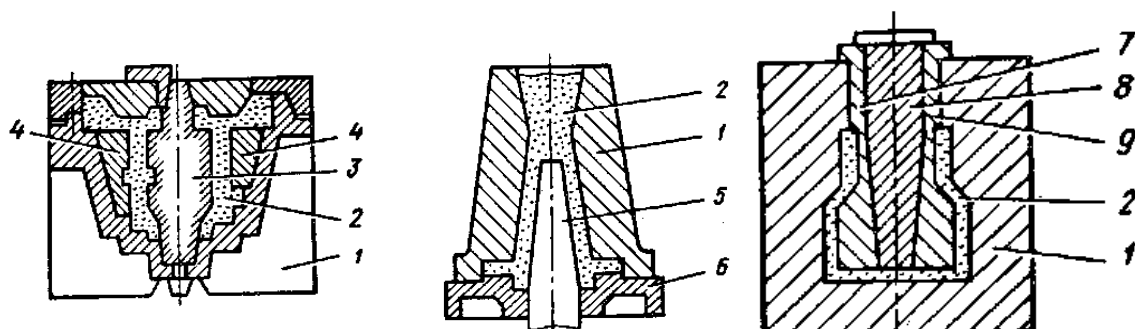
Последовательность операций изготовления отливок в кокиль:
